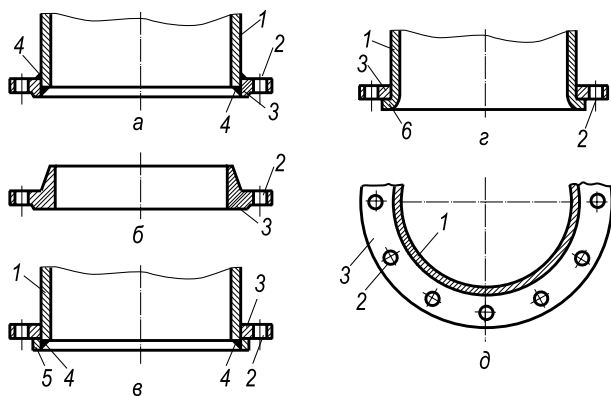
Стальные фланцы: а — плоский приварной; б — приварной встык; в — свободный на приварном кольце; г — свободный на отбортованной трубе; д — на приварном кольце и отбортованной трубе
